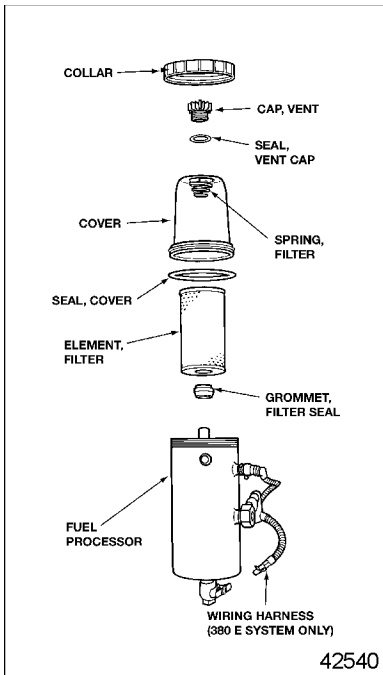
Ensamble del procesador de combustible Fuel Pro 382E
